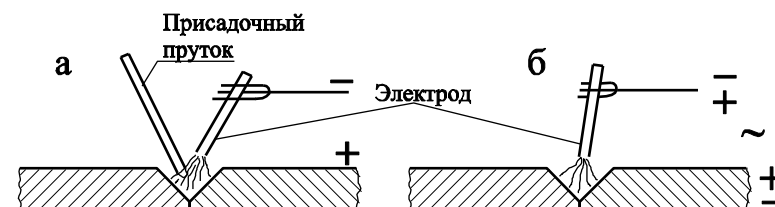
Способы сварки: а - Бенардоса, б - Славянова
